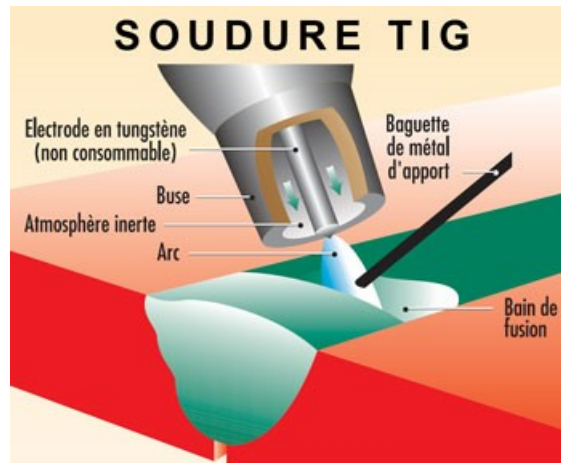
Principe du soudage TIG, (<http://www.outiland.fr/le-poste-a-souder-a-l-arc-mma-mag-mig-tig.html>).
